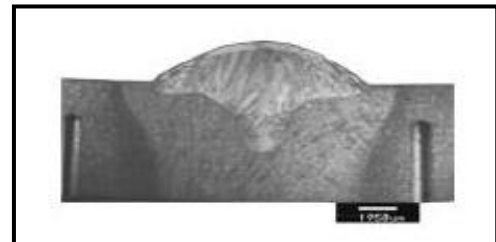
macrographie d'un cordon de soudure [23].
